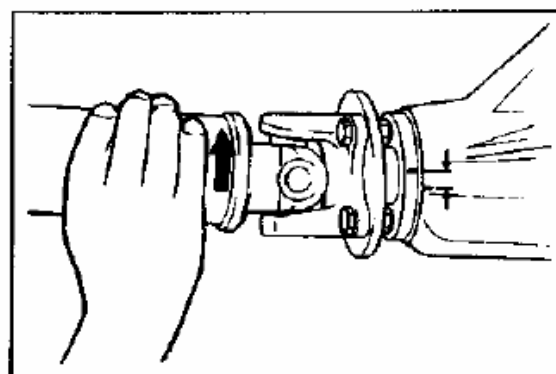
Проверка люфта ведущей шестерни главной передачи
